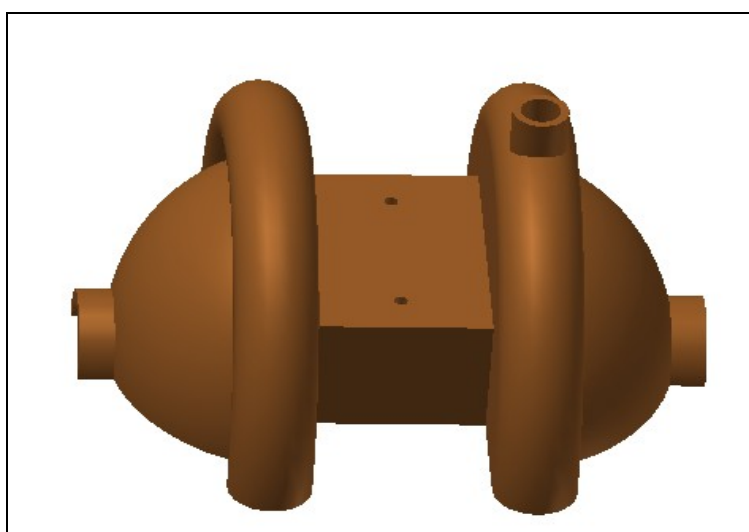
Carcasa superior turbocompresor, pieza
